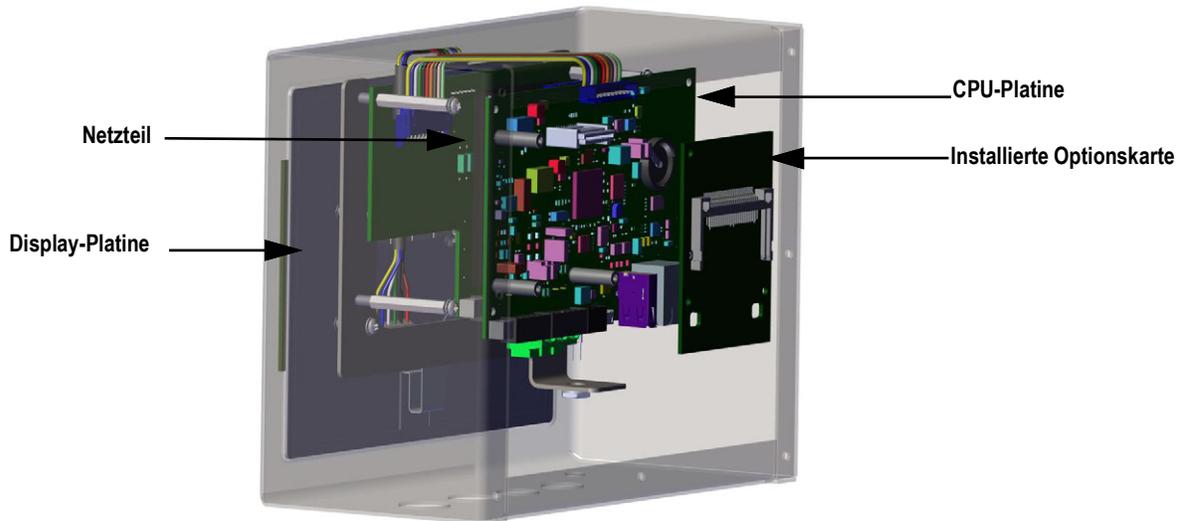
Positionen der Platinen in der Universal-Montagehalterung
